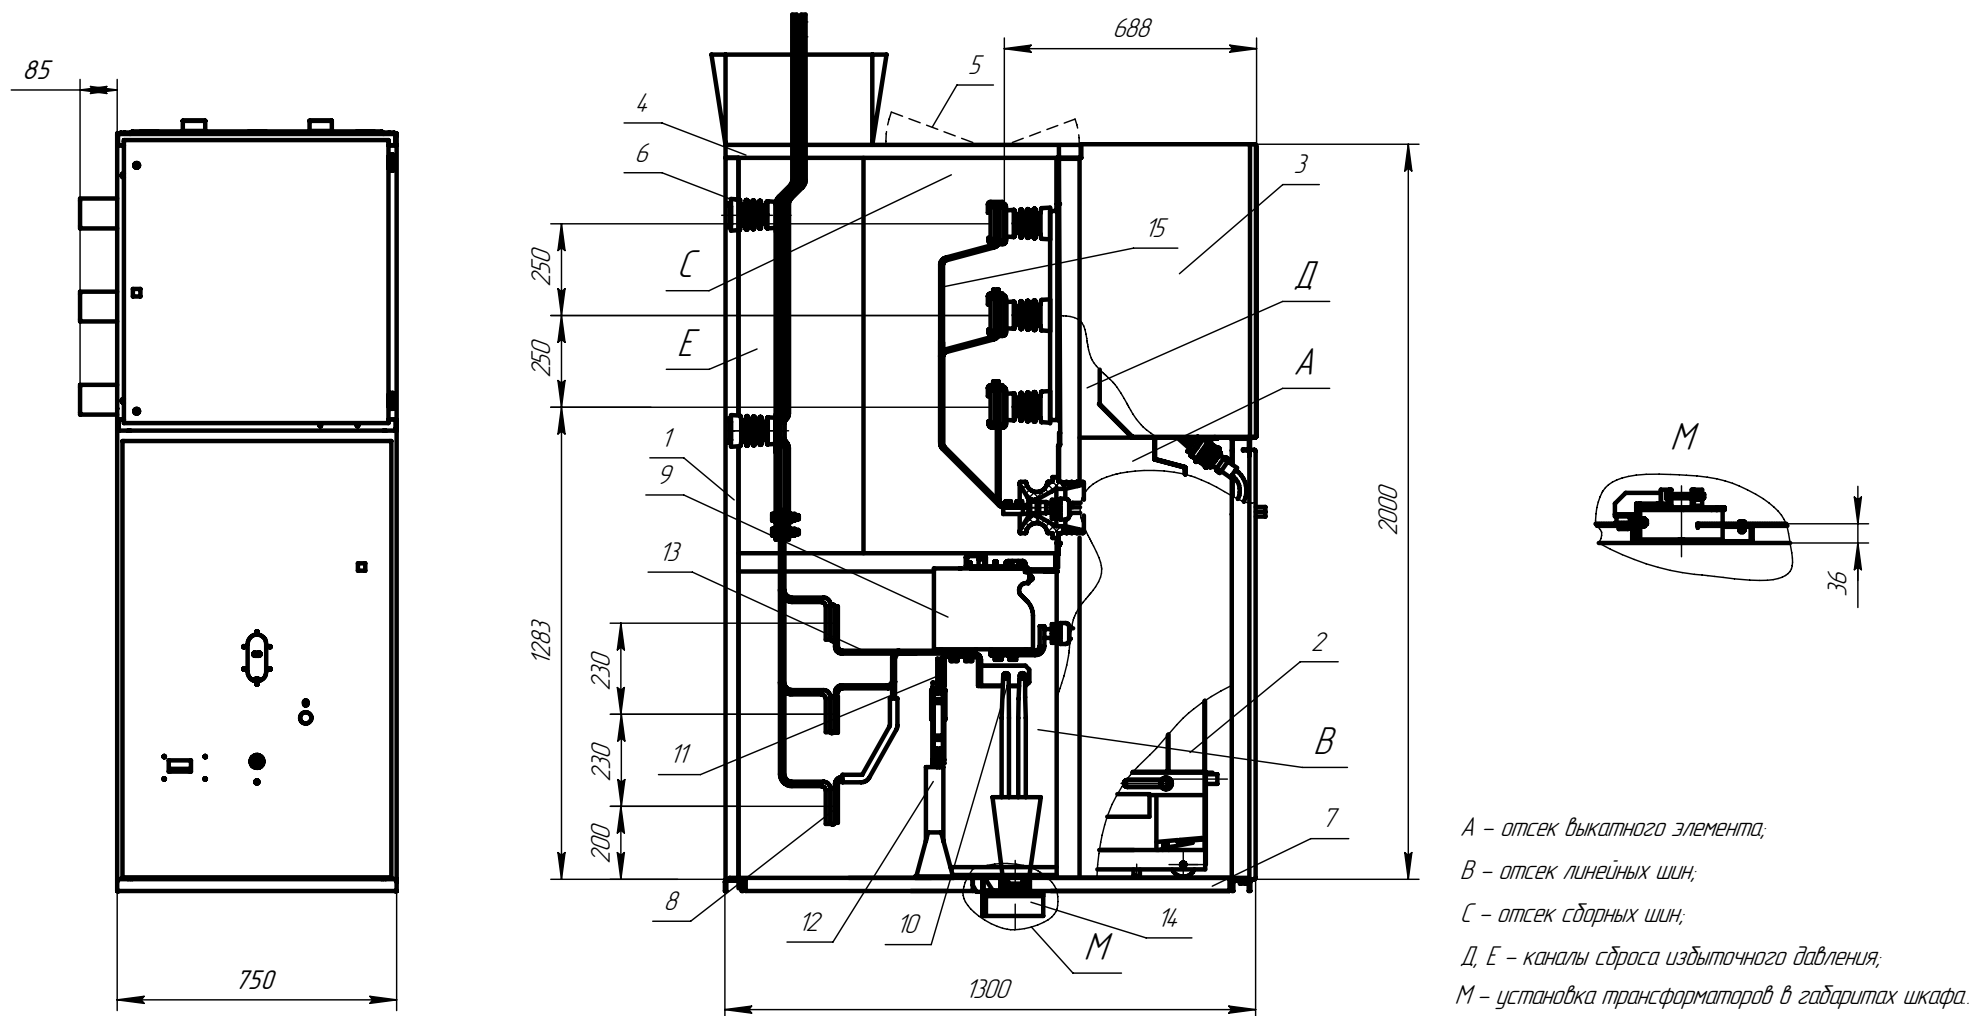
Габаритные, установочные, присоединительные размеры шкафов.
